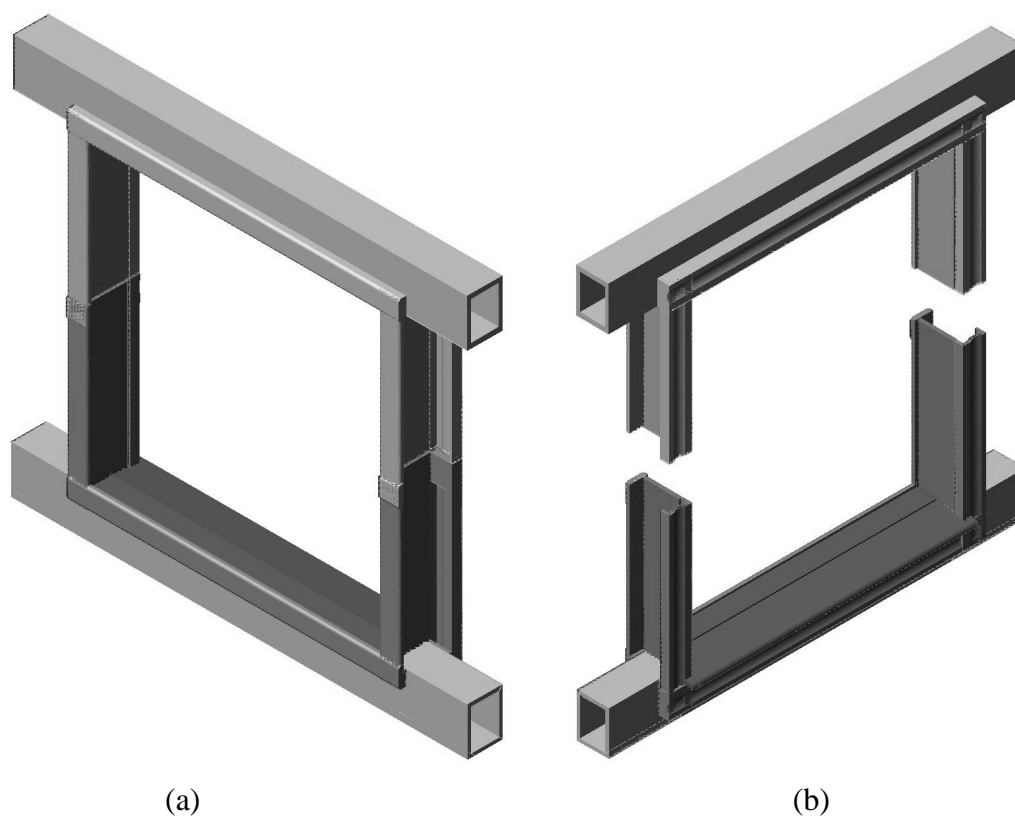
Projeto 04, vista 3d da face interna (a) e vista 3d da face externa (b).
